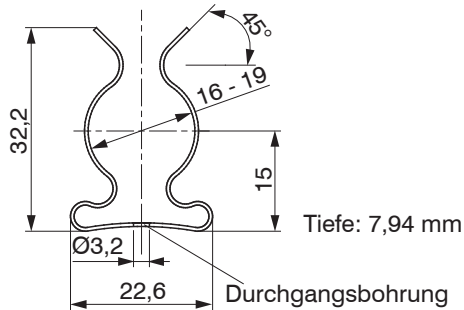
Maßzeichnung für Montageklammer, Abmessungen in mm
